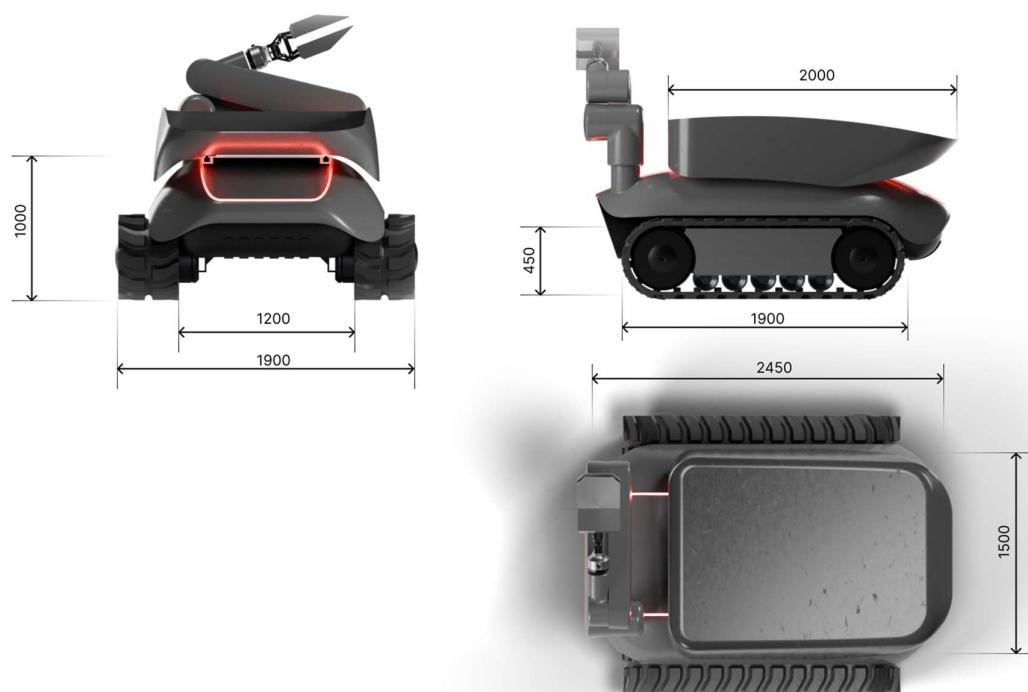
Tvarování robota s nástavbou pro sypké materiály, pohled zezadu
